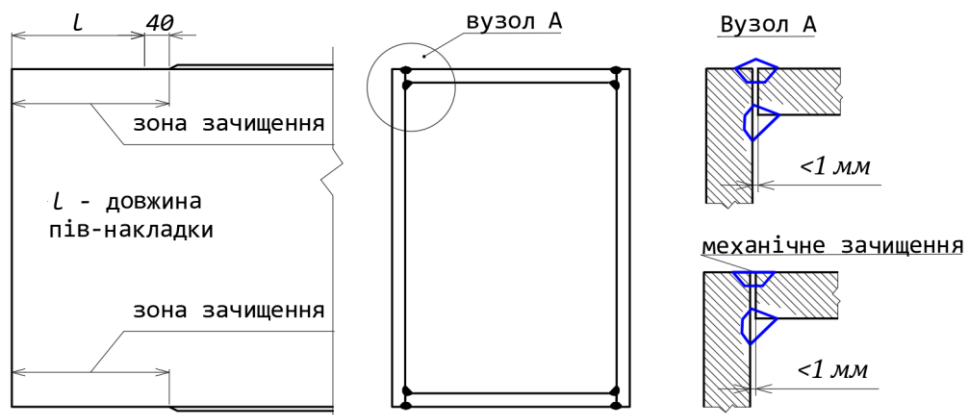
Схема обробки посилення шва зварювання коробчастого перерізу
